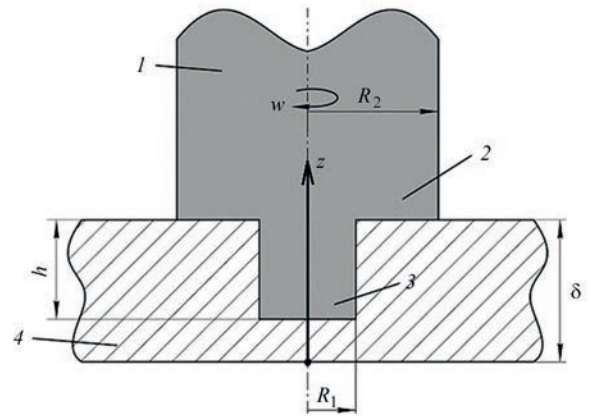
Схема робочого інструменту при ЗТП: 1 – інструмент; 2 – плече; 3 – пластина; 4 – штир
